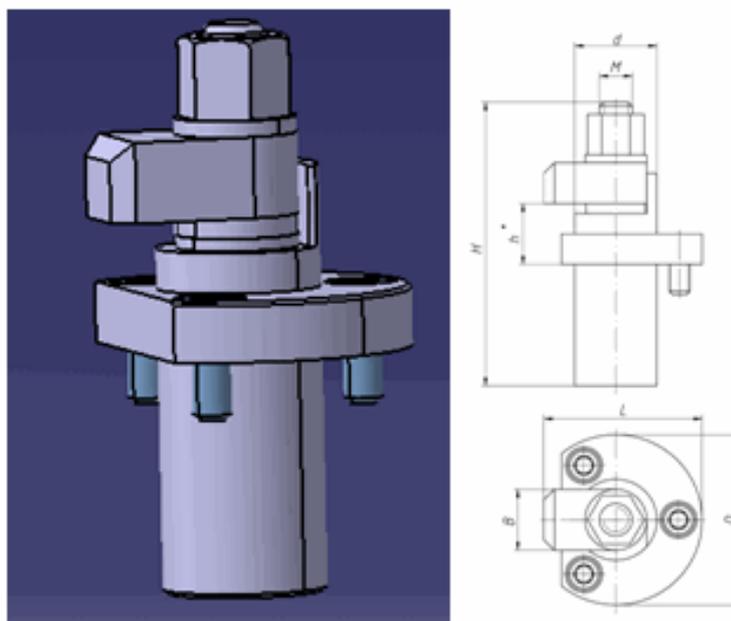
Зажим прихватом Г-образным с креплением опорной втулки сверху
